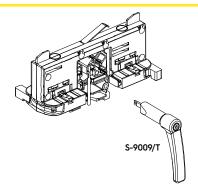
Cablaggio dell'adattatore *Pic. 1 Adapter wiring
